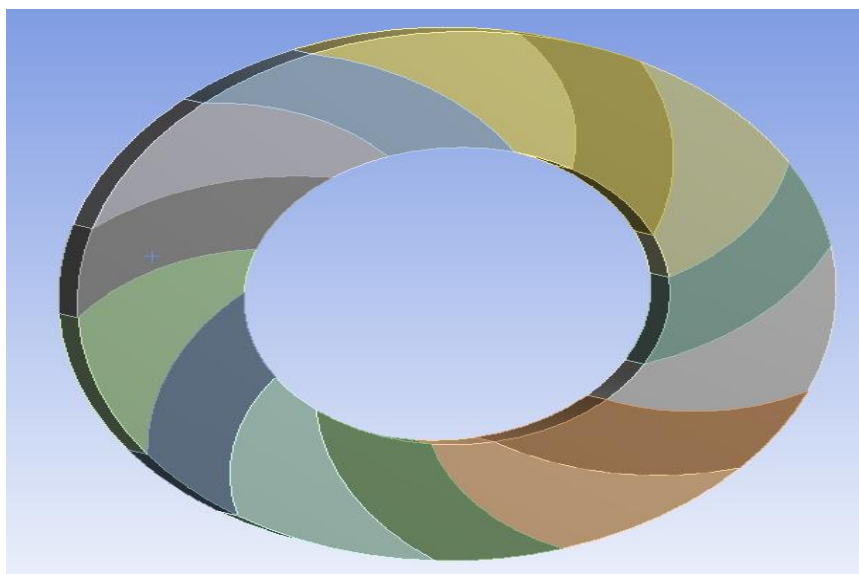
Геометрическая модель рабочей поверхности абразивного инструмента
